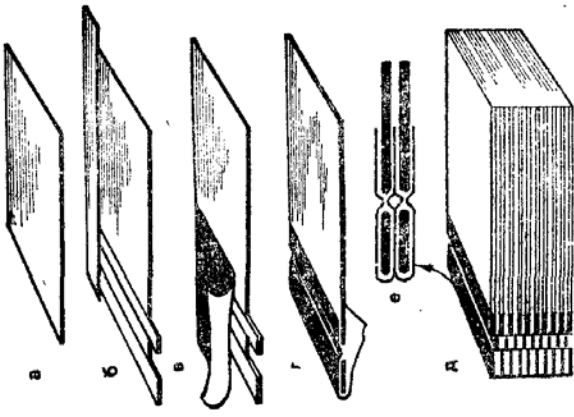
Схема процесса изготовления альбомных листов для последующей сборки на шнурах: а — картонная заготовка; б — расположение деталей на шаблоне; в — накладка тканевой полоски; г — загибка тканевой полоски и наклейка с оборотной стороны шарнира; д — готовый блок
